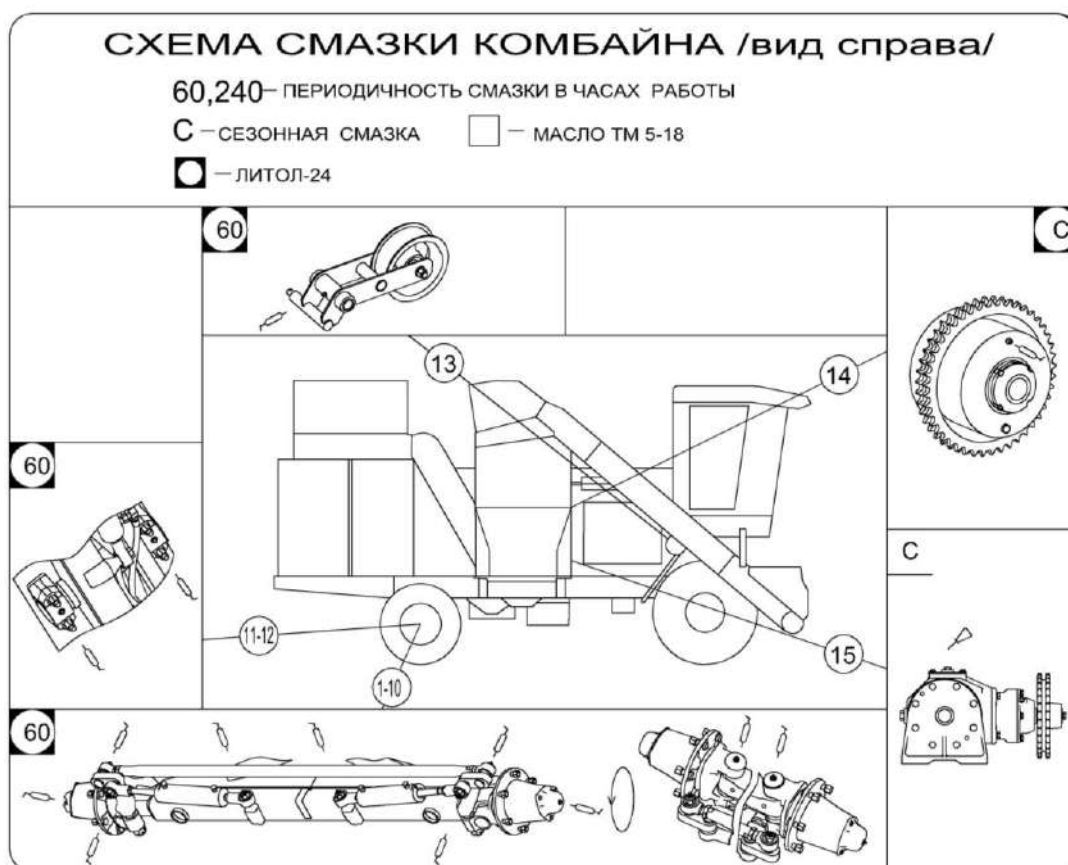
Схема смазки комбайна (вид справа)
